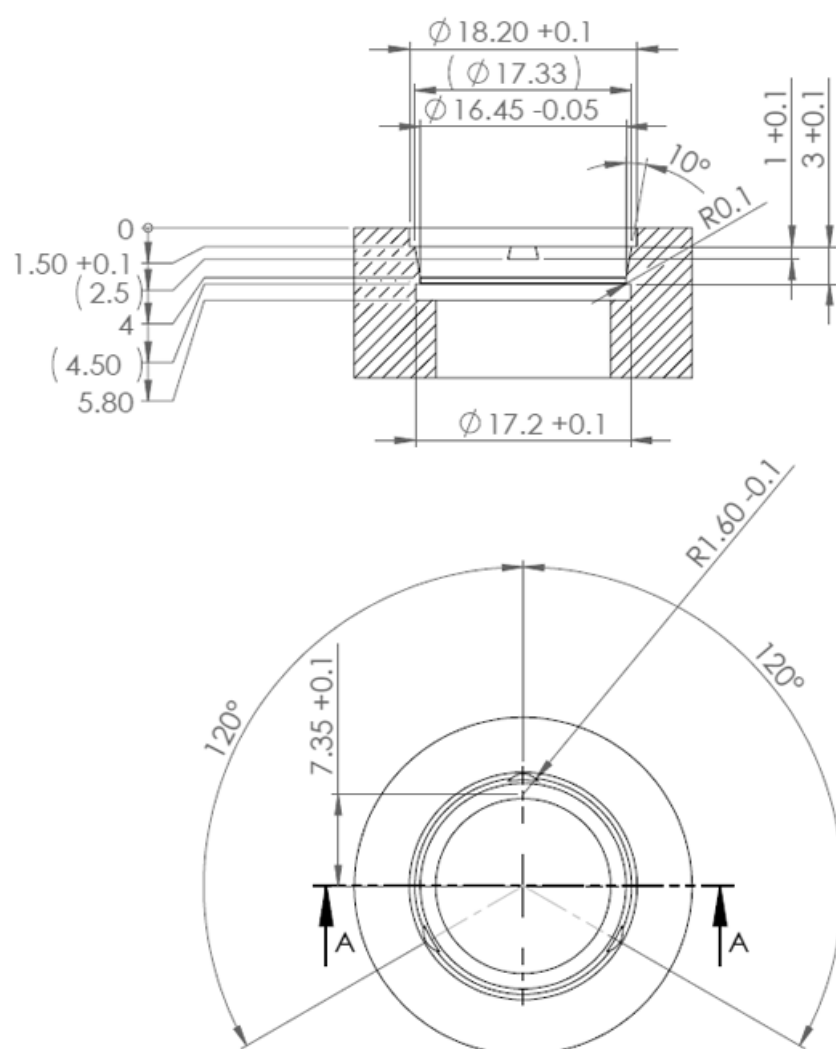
Desenho de dimensões: Furo da peça para montagem da variante especial do MDS D522
